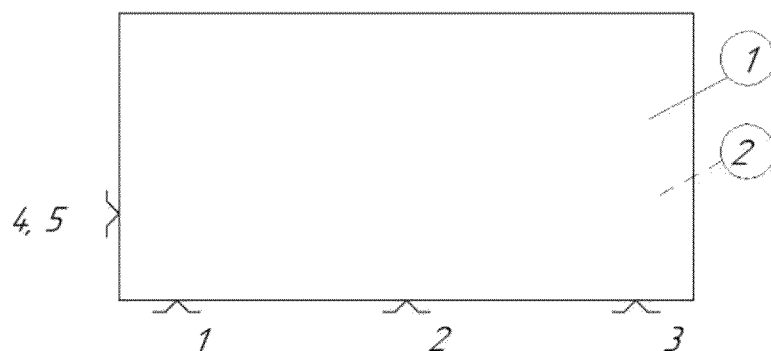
Схема встановлення деталі на чорнові бази
